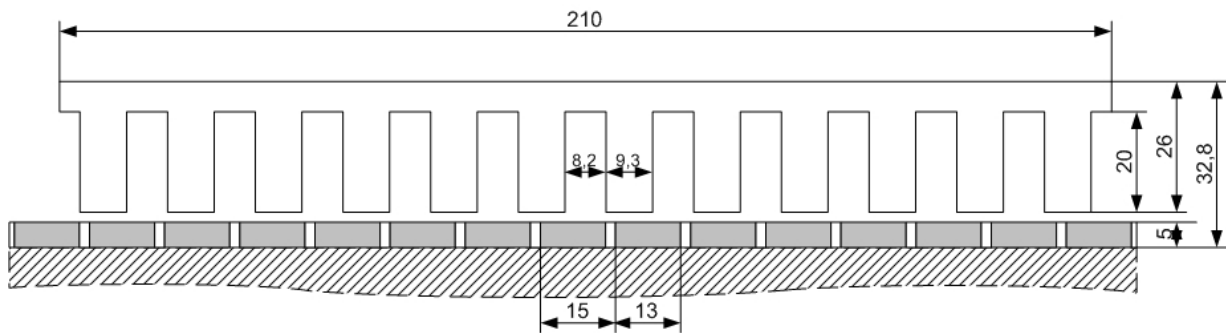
Blechschnitt des Prüflings (Maß in mm)
